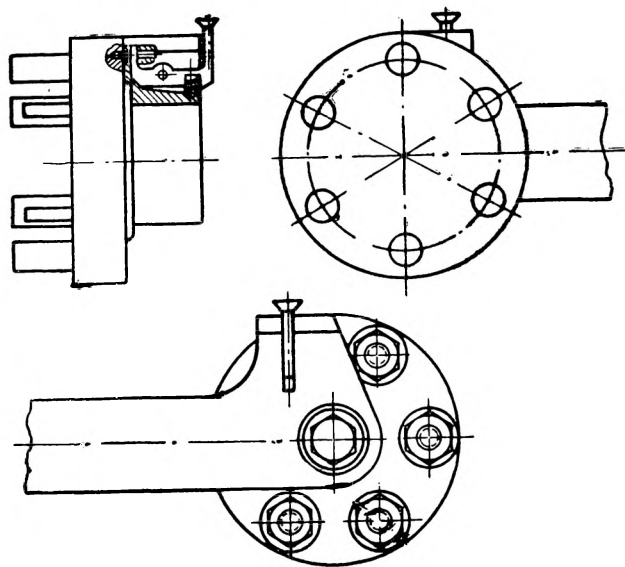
Многорезцовая головка к суппорту токарного станка.
